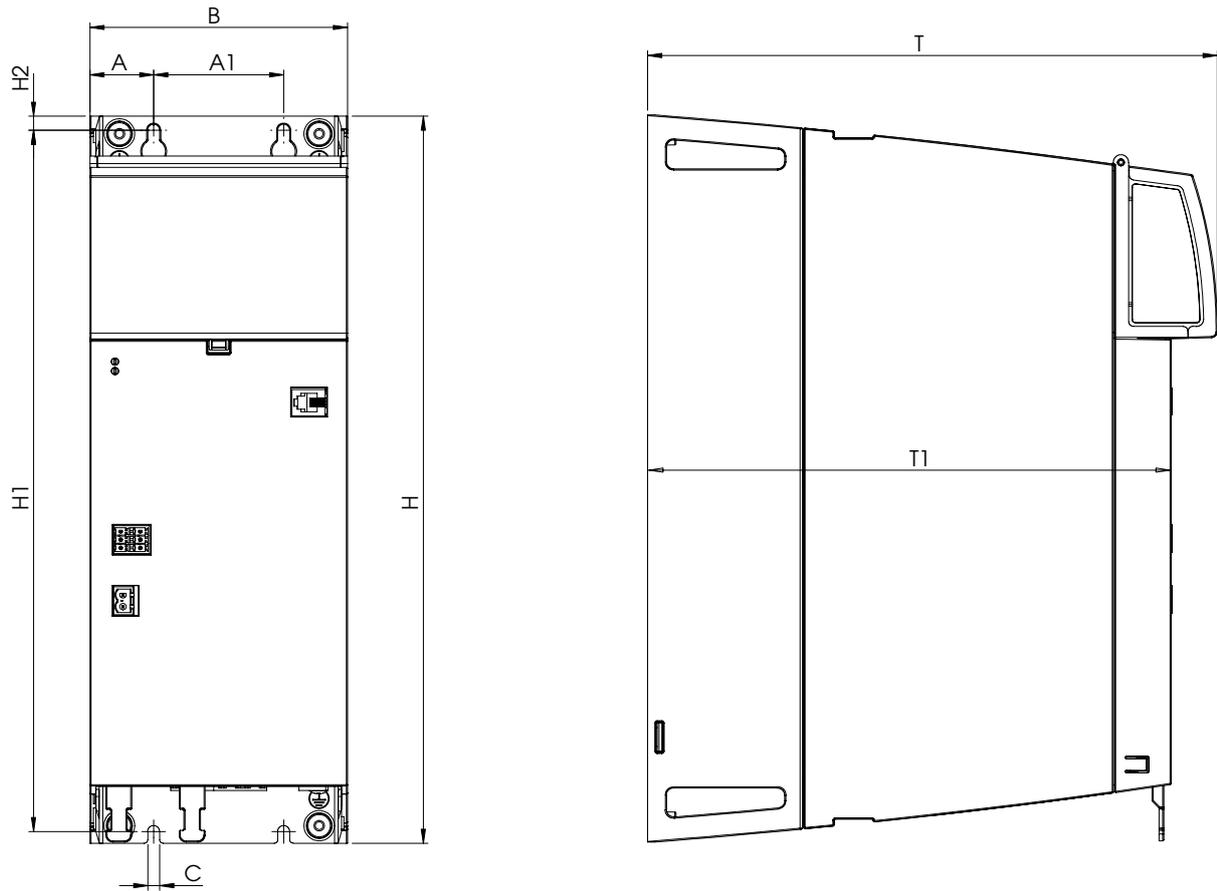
JM-3000 电源装置 BG2 尺寸图 (尺寸请参见表表 2.1)
